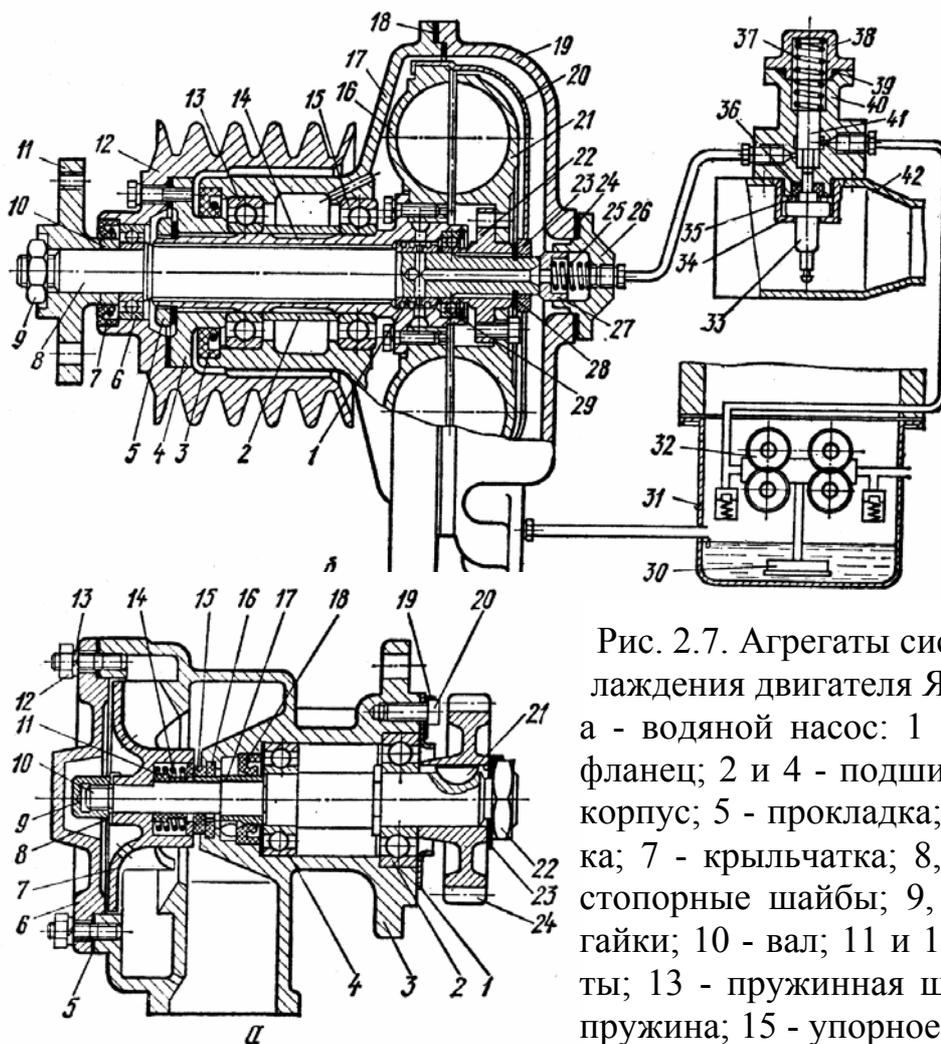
Агрегаты системы охлаждения двигателя ЯМЗ-240Б: а - водяной насос: 1 - упорный фланец; 2 и 4 - подшипники; 3 - корпус; 5 - прокладка; 6 - крышка; 7 - крыльчатка; 8, 19 и 23 - стопорные шайбы; 9, 12 и 22 - гайки; 10 - вал; 11 и 18 - манжеты; 13 - пружинная шайба; 14 - пружина; 15 - упорное кольцо
